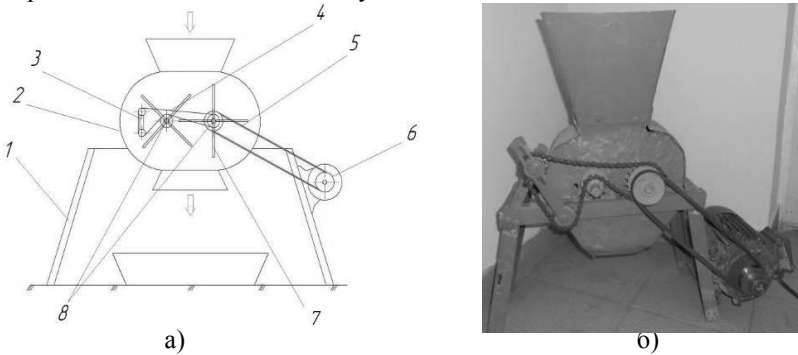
Схема (а) та загальний вигляд (б) пристрою для подрібнення частинок сапропелевих добрив: 1 - корпус; 2 - кожух; 3 - натяжний пристрій; 4 - ланцюгова передача; 5 - пасова передача; 6 - двигун; 7 - лопаті; 8 - ротор
